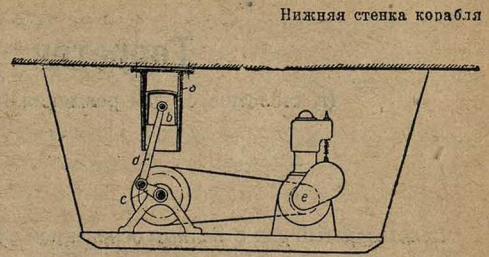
„Схема механизма летательного аппарата, способного, якобы, подниматься вертикально вверх: а — цилиндр; б — поршень; с — кривошип; д — шатун; е — мотор.“
